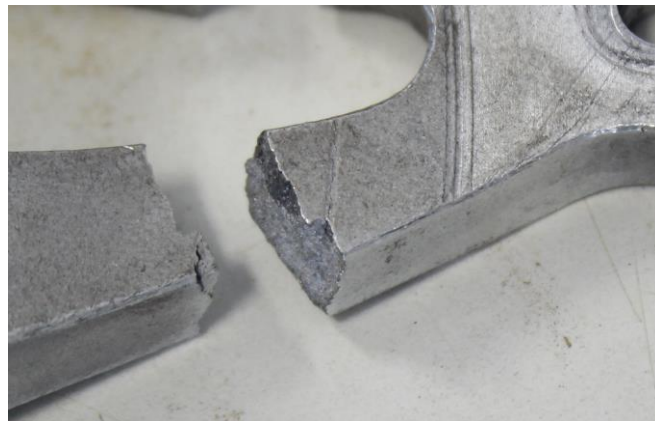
Foto do revelador de trinca aplicado na flange esquerda.
